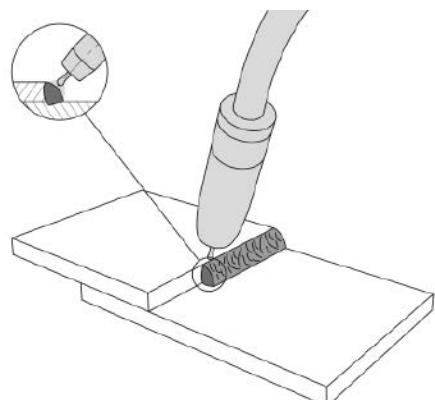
Вылет сварочной проволоки.
